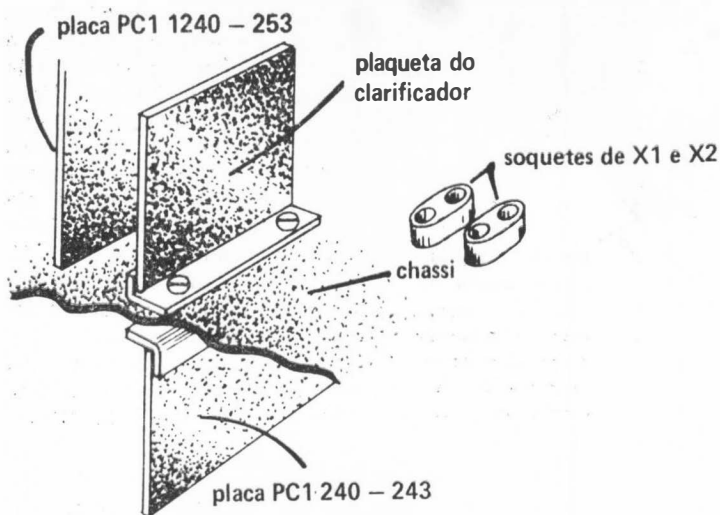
Instalação do clarificador junto ao oscilador a XTAL. O chassi está representado em corte, com o equipamento visto de frente, pelo lado esquerdo.
